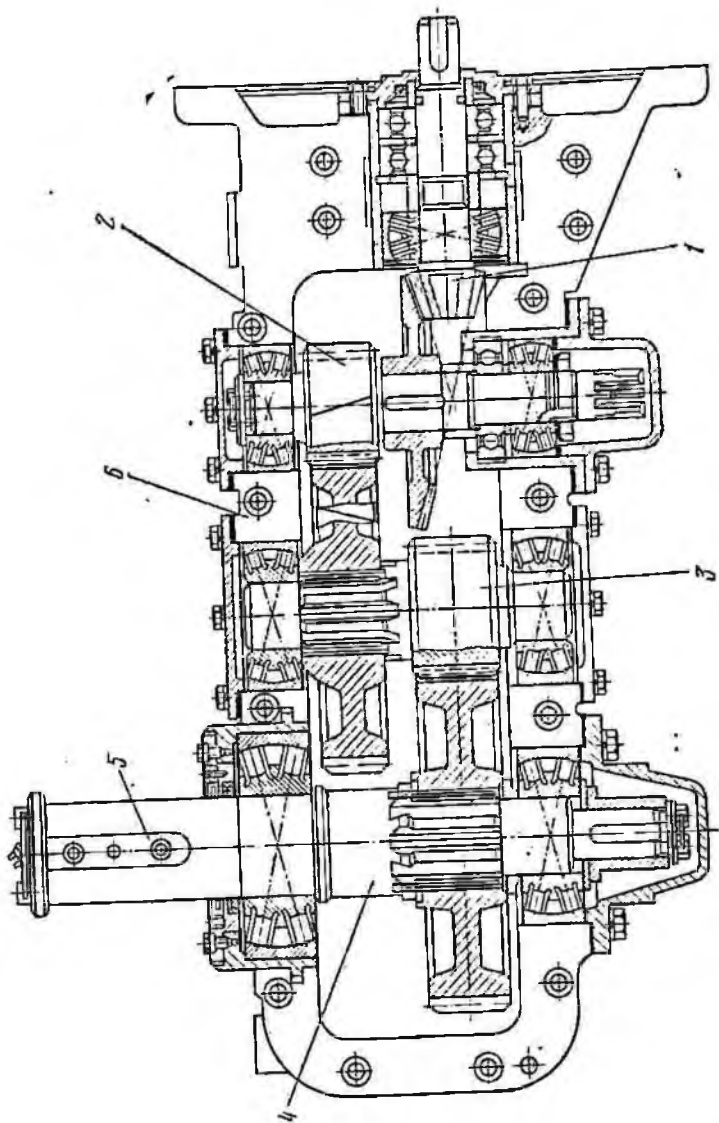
Продольный разрез редуктора привода СП63/К2-02
